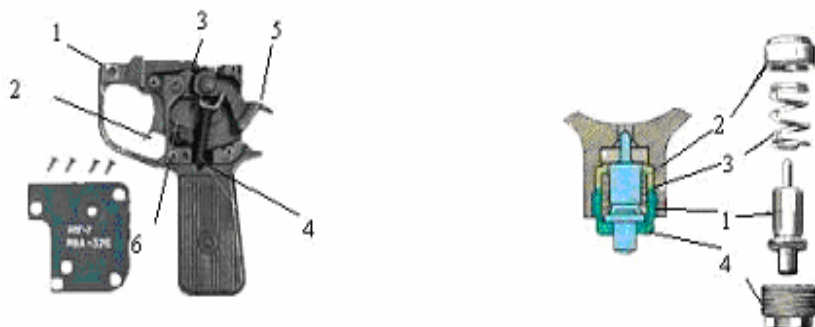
(а,б) – Ударно-спусковий та бойковий механізми: а) 1 – корпус; 2 – спусковий гачок; 3 – шептала; 4 – стрижень з бойовою пружиною; 5 – гачок; 6 – запобіжник; б) 1 – бойок; 2 – опорна втулка; 3 – пружина бойка; 4 – ніпель
